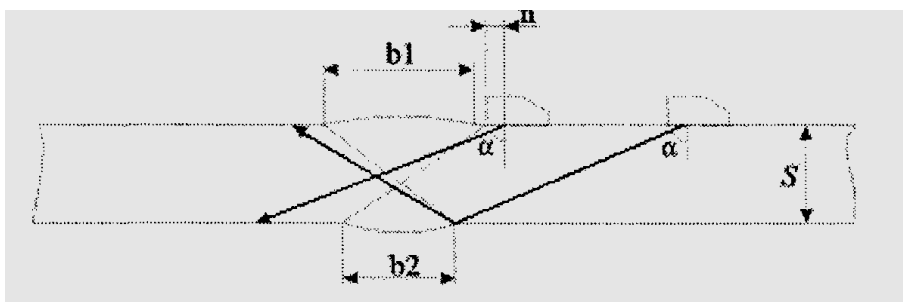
Схема сканирования сварного соединения
